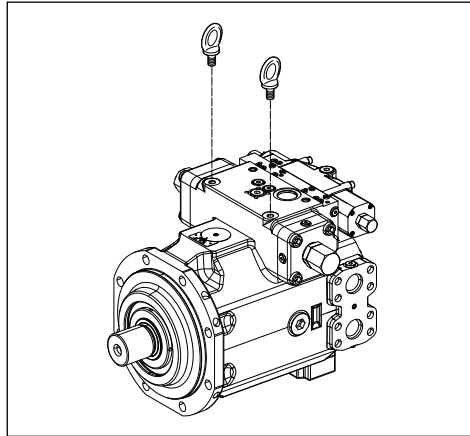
Befestigung der Ringschrauben im Gehäuse
